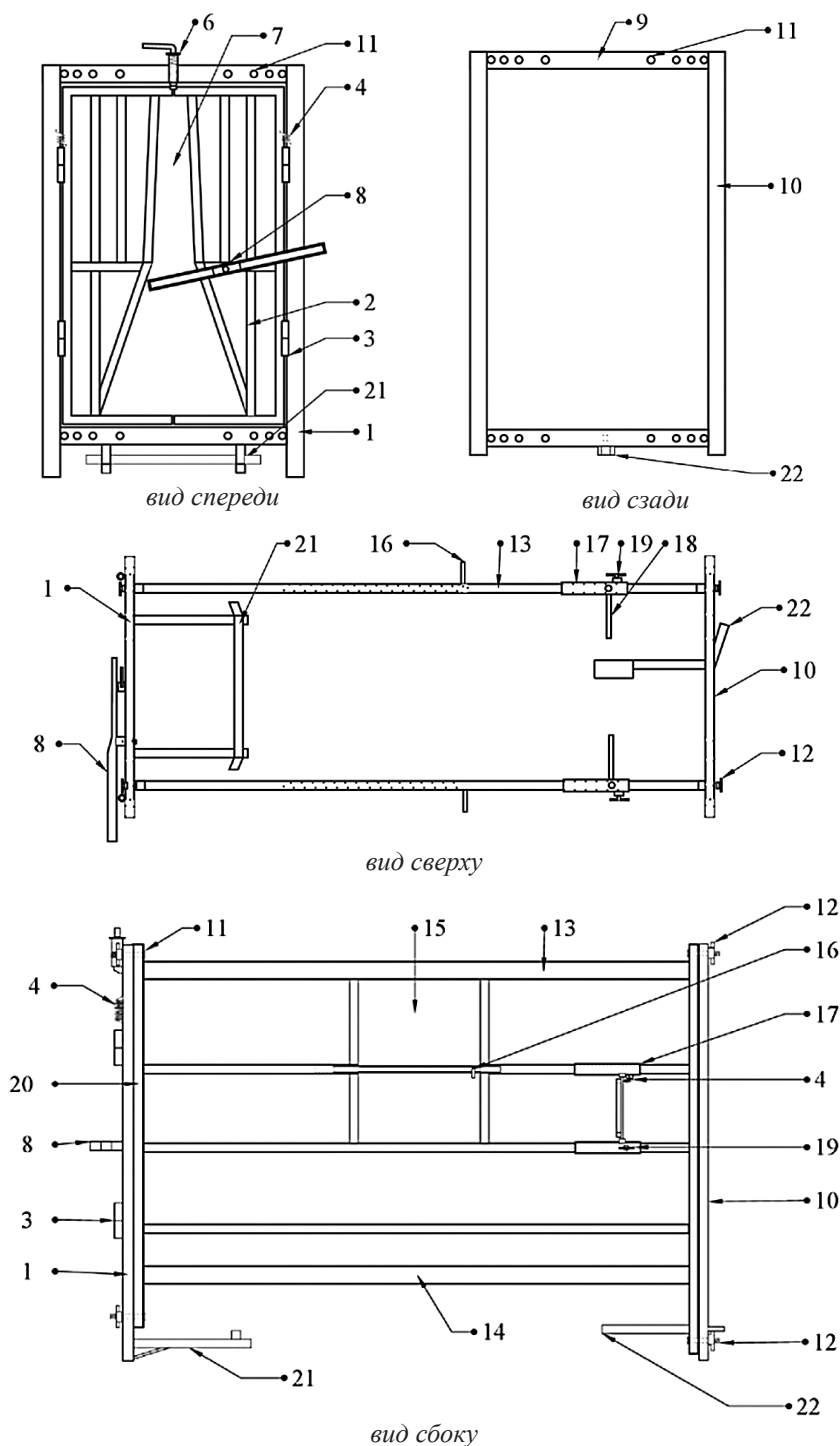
Усовершенствованная конструкция разборной клетки для овец
